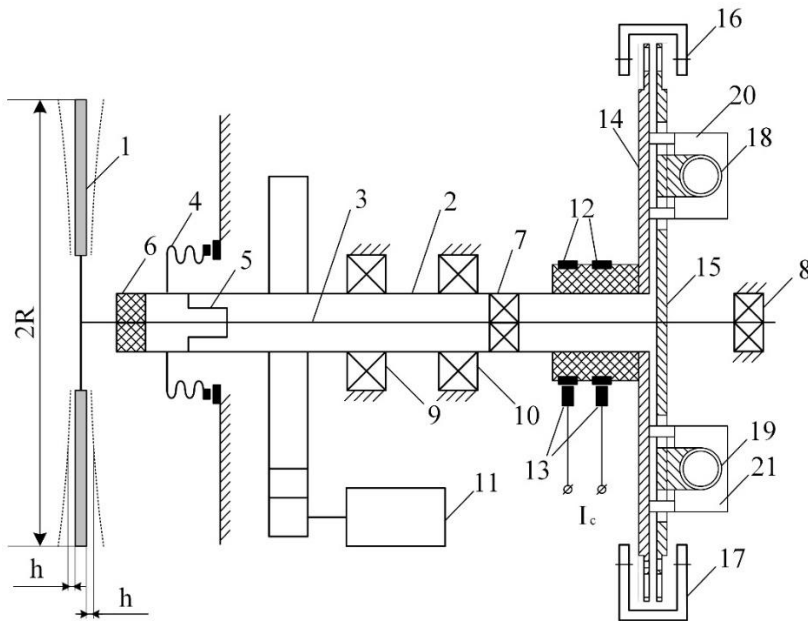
Конструкція механічної частини ротаційного концентрометра паперової пульпи з магнітоелектричним компенсатором моменту в'язкісного тертя. 1 - чутливий елемент дископодібної форми; 2 - основний порожнистий вал приладу; 3 - вал чутливого елемента; 4 - ущільнення основного порожнистого вала з силфону і кільцевих вставок зі сплаву карбід вольфраму-кобальт; 5 - гнучке ущільнення з поздовжньо гофрованої тонкостінної трубки; 6 - захисне еластичне ущільнення; 7, 8 - підшипники вала чутливого елемента; 9, 10 - підшипники основного порожнистого вала; 11 - двигун з живленням від частотного перетворювача; 12 - струмопідвідні кільця; 13 - графітокомпозитні щітки; 14 - диск з прорізами на основному валу приладу; 15 - диск з прорізами на валу чутливого елемента; 16 - оптопара з відкритим оптичним каналом для вимірювання кутового зміщення дисків 14 і 15; 17 - оптопара з відкритим оптичним каналом для фіксації початку відліку; 18, 19 - навитки магнітоелектричного перетворювача, закріплені на диску 15; 20, 21 - магнітні системи, закріплені на диску 14.
